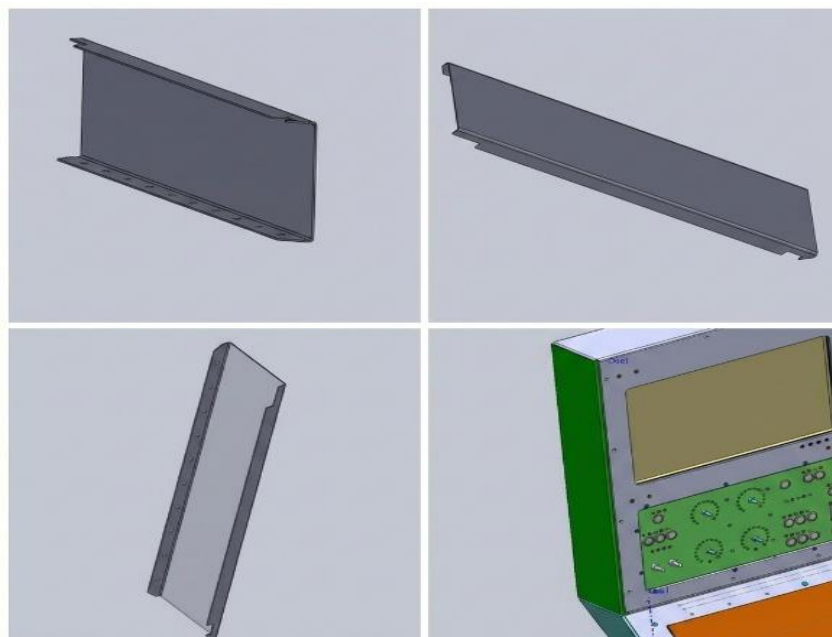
Плоска листовая деталь з фрезерованими та свердловинними отворами
